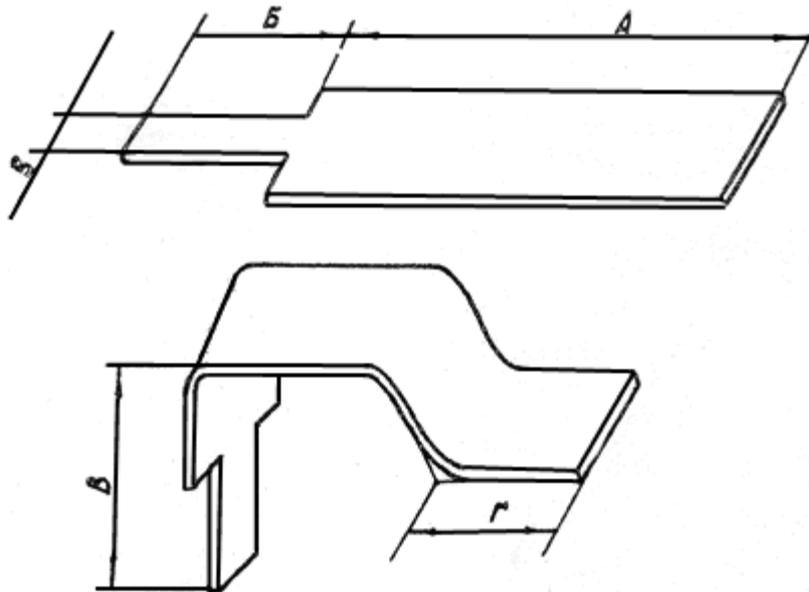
Приспособление для пайки ушков пластин с соединительными полосами
